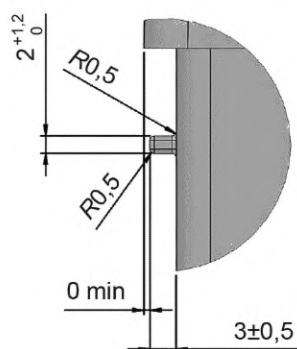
Размеры выступа для ЗРО (деталь Y), приведенного на рисунках 25 и 26
